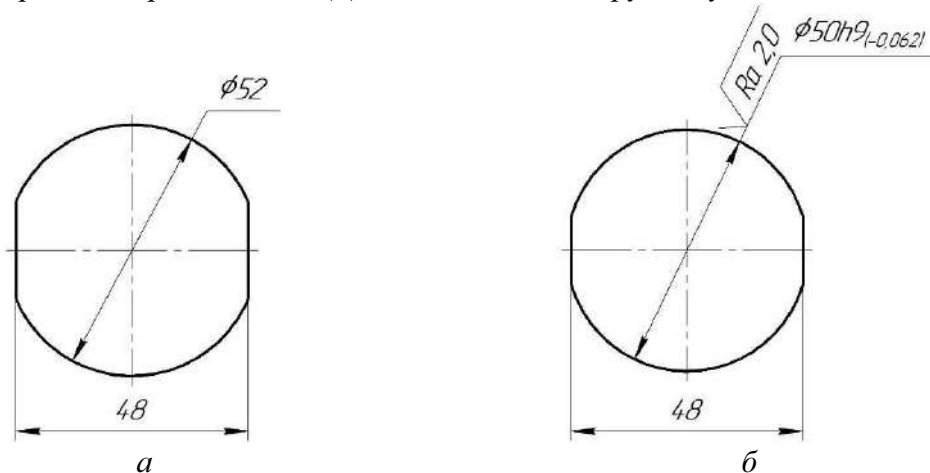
Ескіз заготовки а) та деталі б) «Поплавок»
